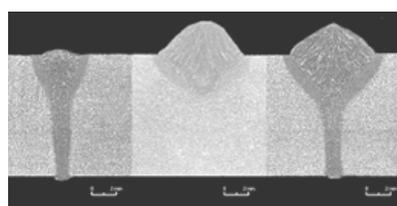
Macrografias de aços soldados com laser (esquerda), MAG (centro) e híbrido laser com MAG (direita) [9]
